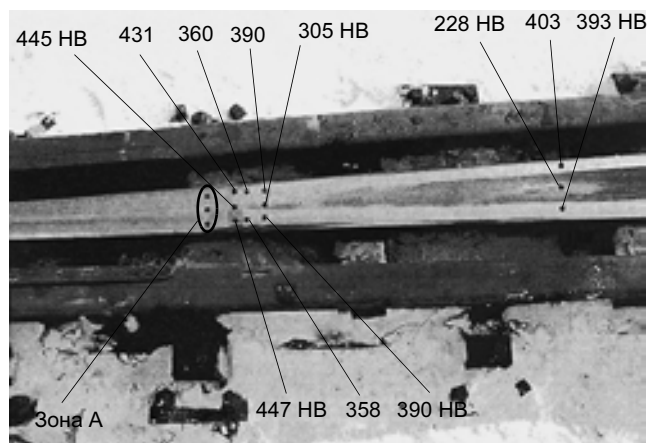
Внешний вид сварной крестовины с результатами замеров твердости по поверхности катания после пропуска 65,2 млн т брутто
